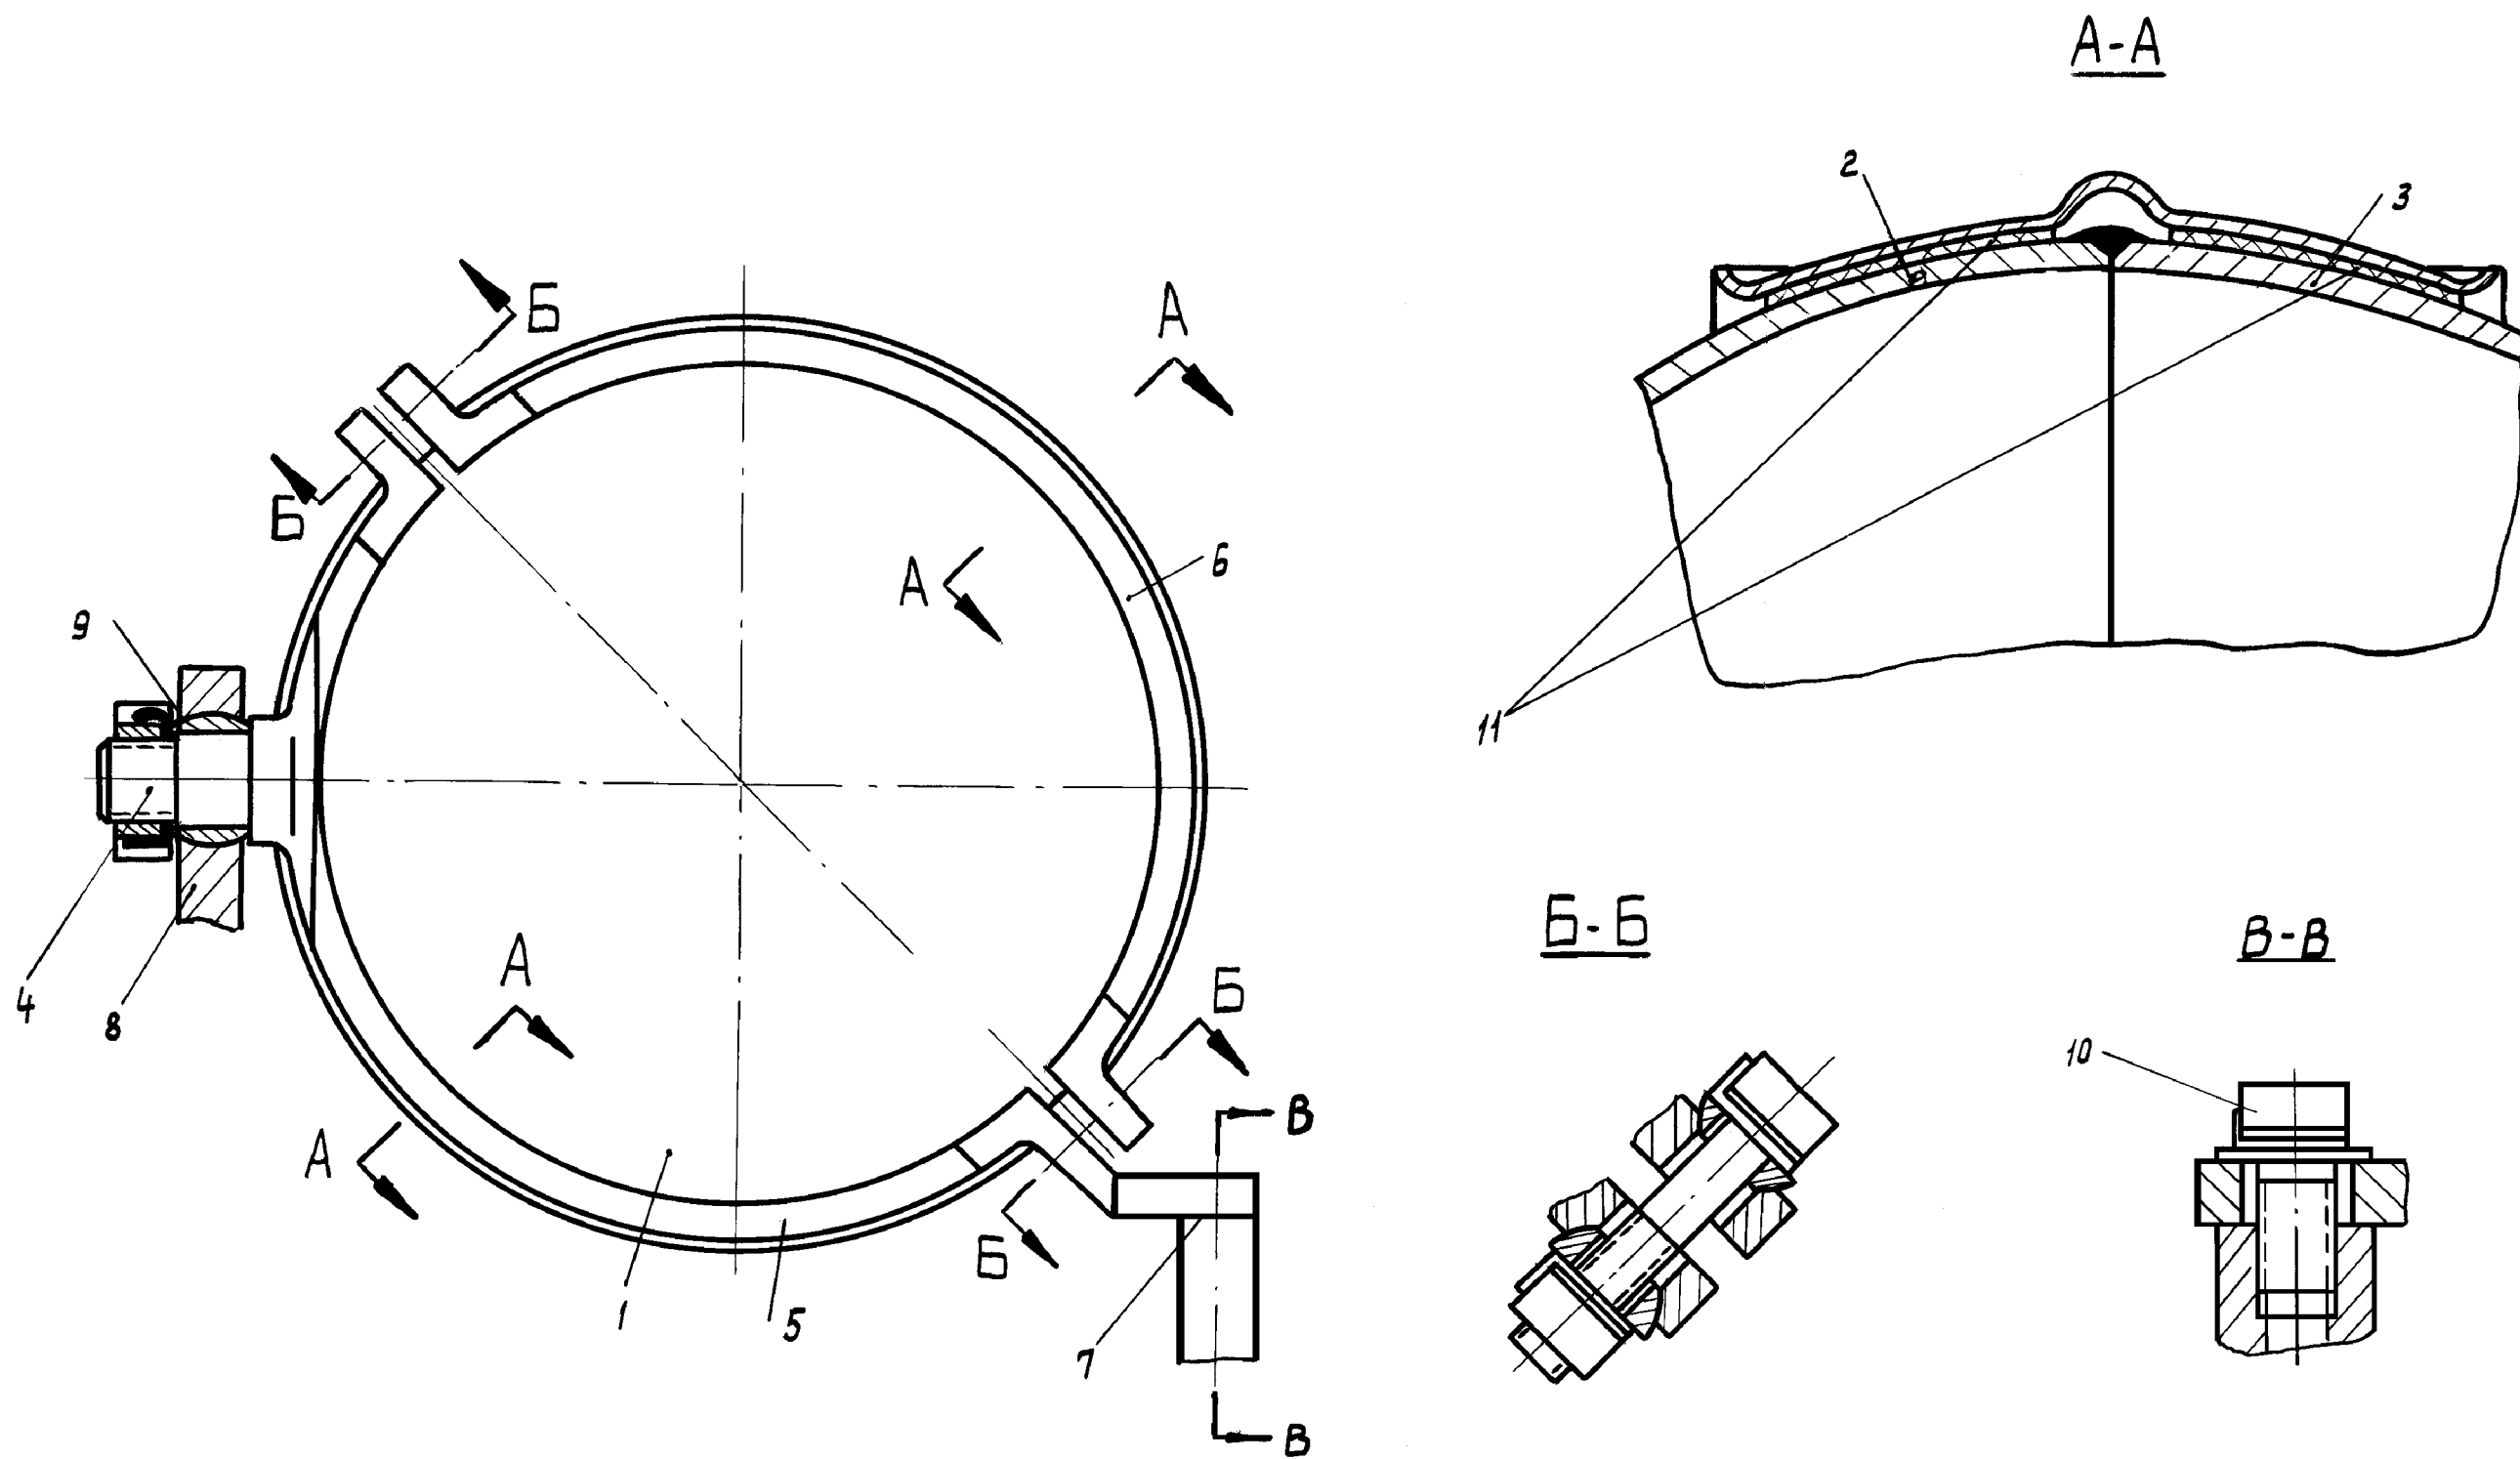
Установка баллона 2530-0100/10072 на двигателе:
